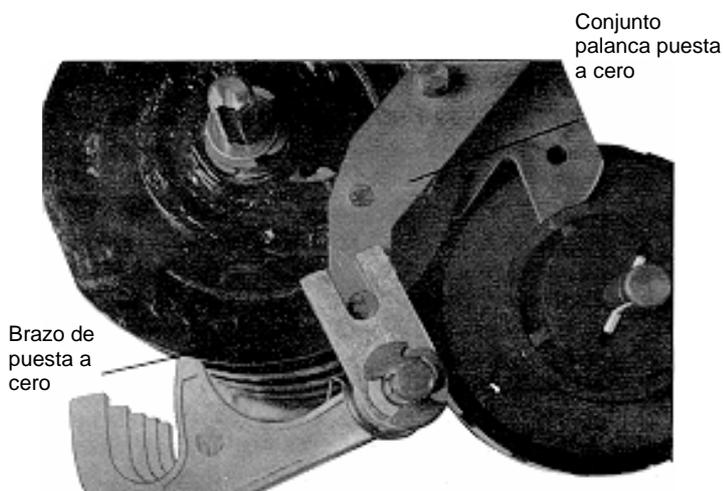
Engranaje pasador conjunto palanca de puesta a cero
